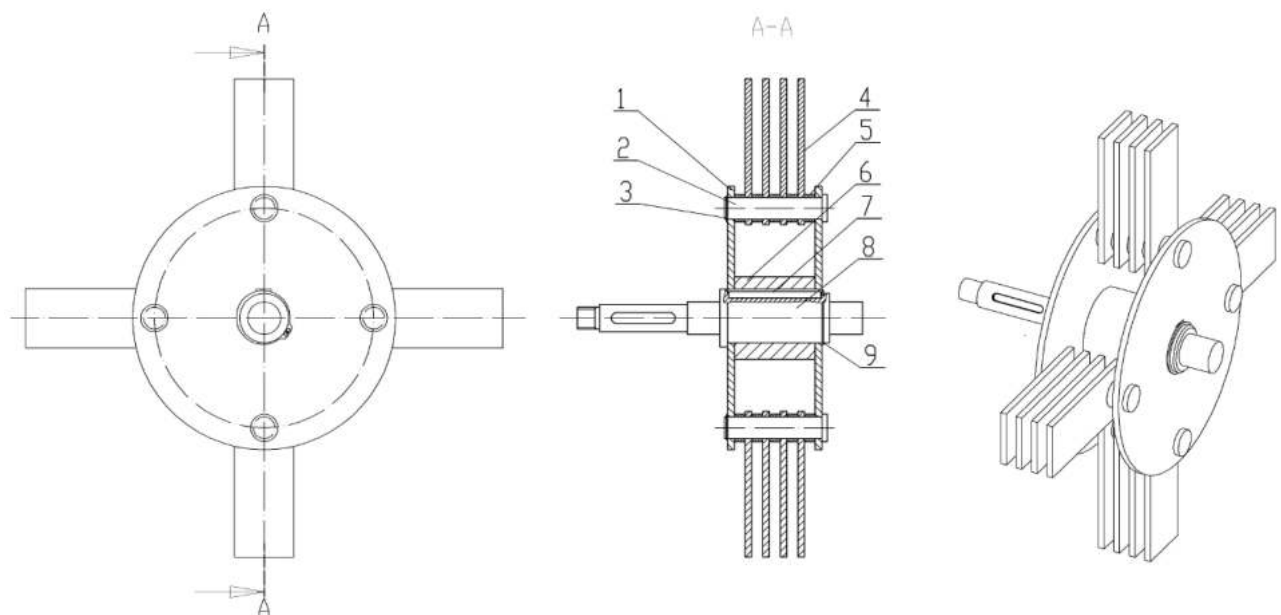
Типовий ротор молоткової дробарки:
